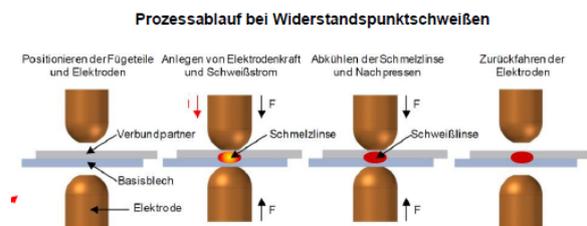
Prozessablauf des Widerstandspunktschweißens
